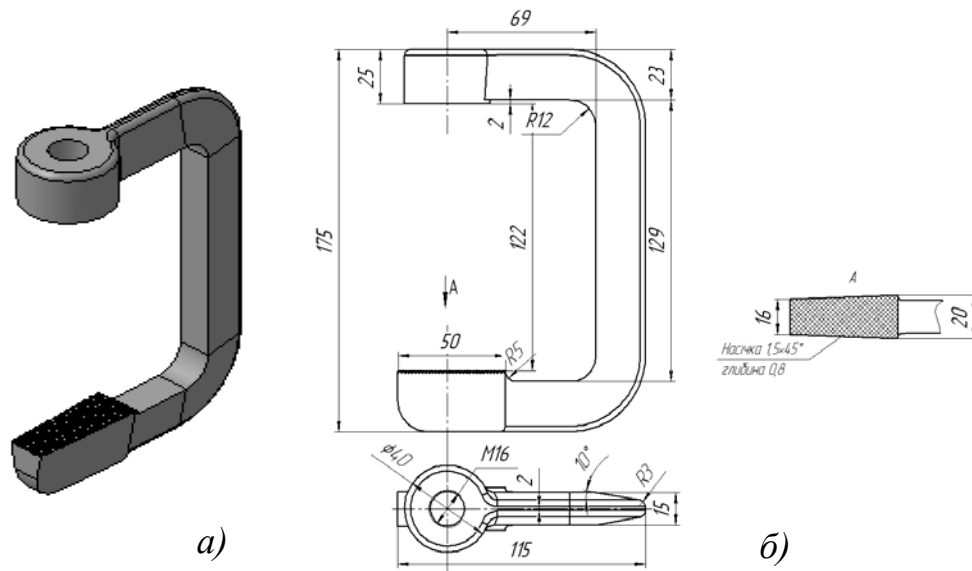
Тривимірна модель (а) та робочий креслений (б) скоби струбцини
